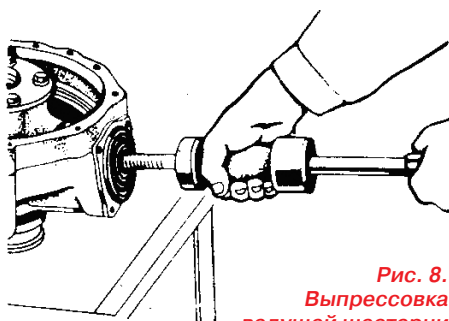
Выпрессовка ведущей шестерни конечной передачи в сборе с подшипником.
